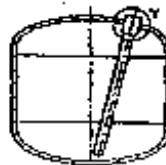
Tube plongeur fixé à la visière d'un récipient horizontal
